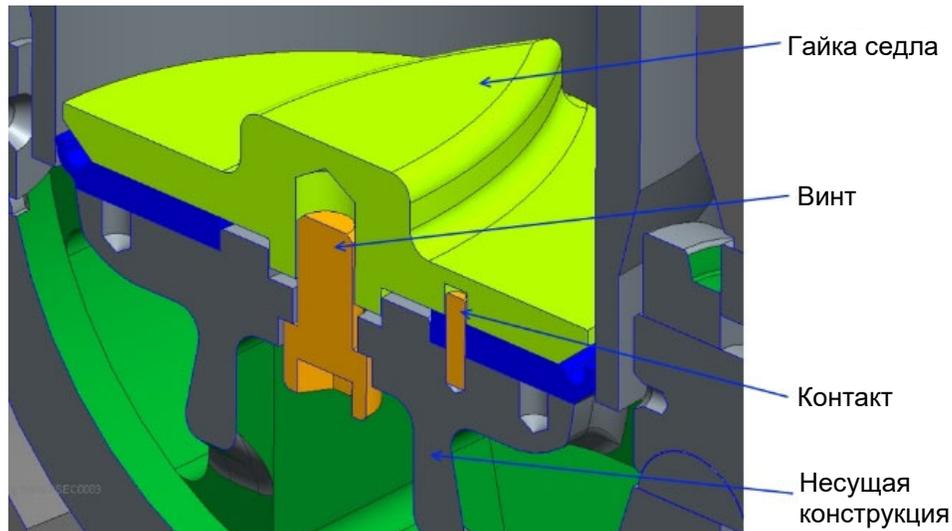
Установите пластину седла и гайку пластины седла
